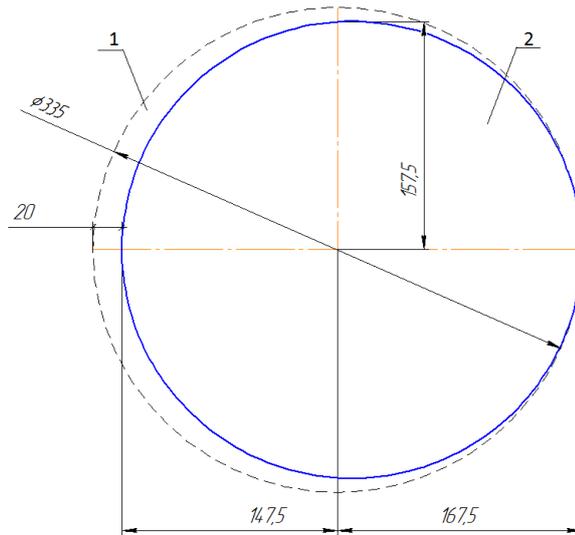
Расчетная и круглая заготовки (1-круглая заготовка, 2-расчетная заготовка)
